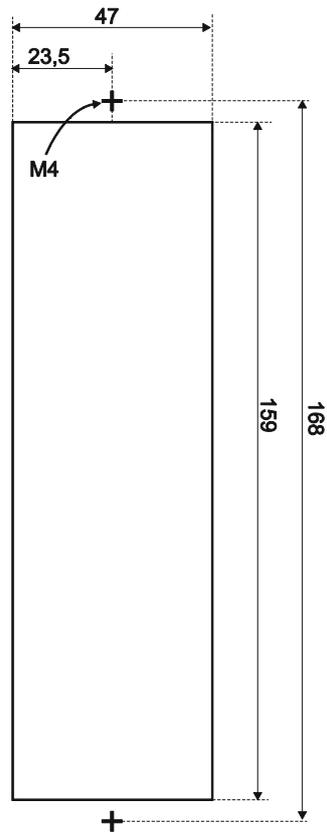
AQ101 Ausschnitt für Türeinbau, Skalierung in Millimeter.
